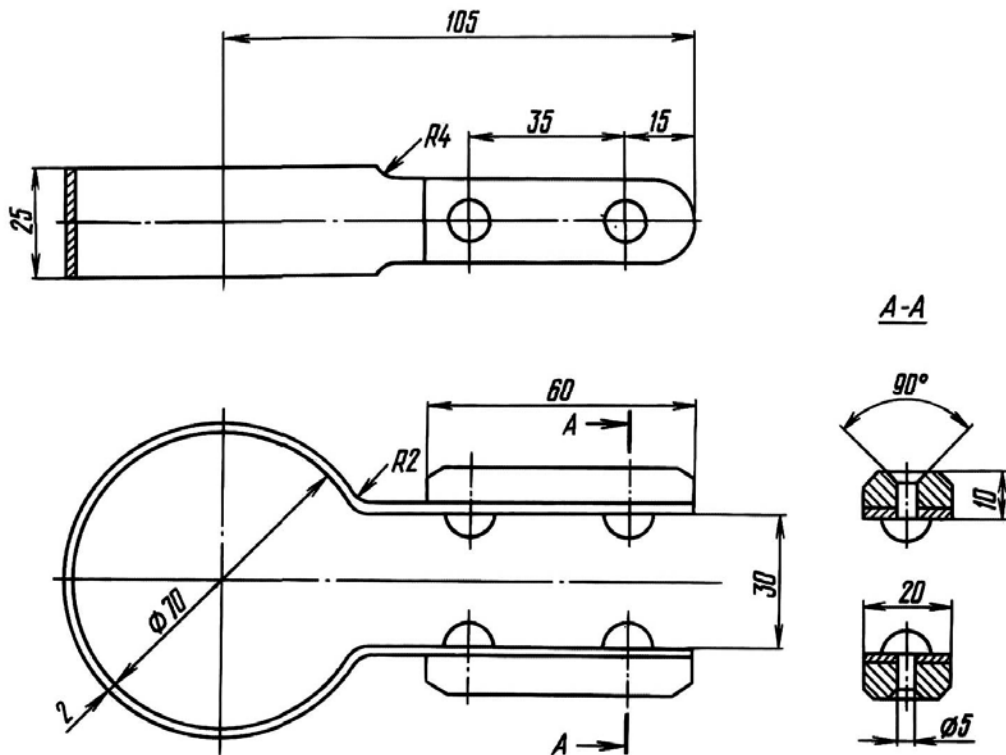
,а. Приспособление для установки поршня в силовой цилиндр
